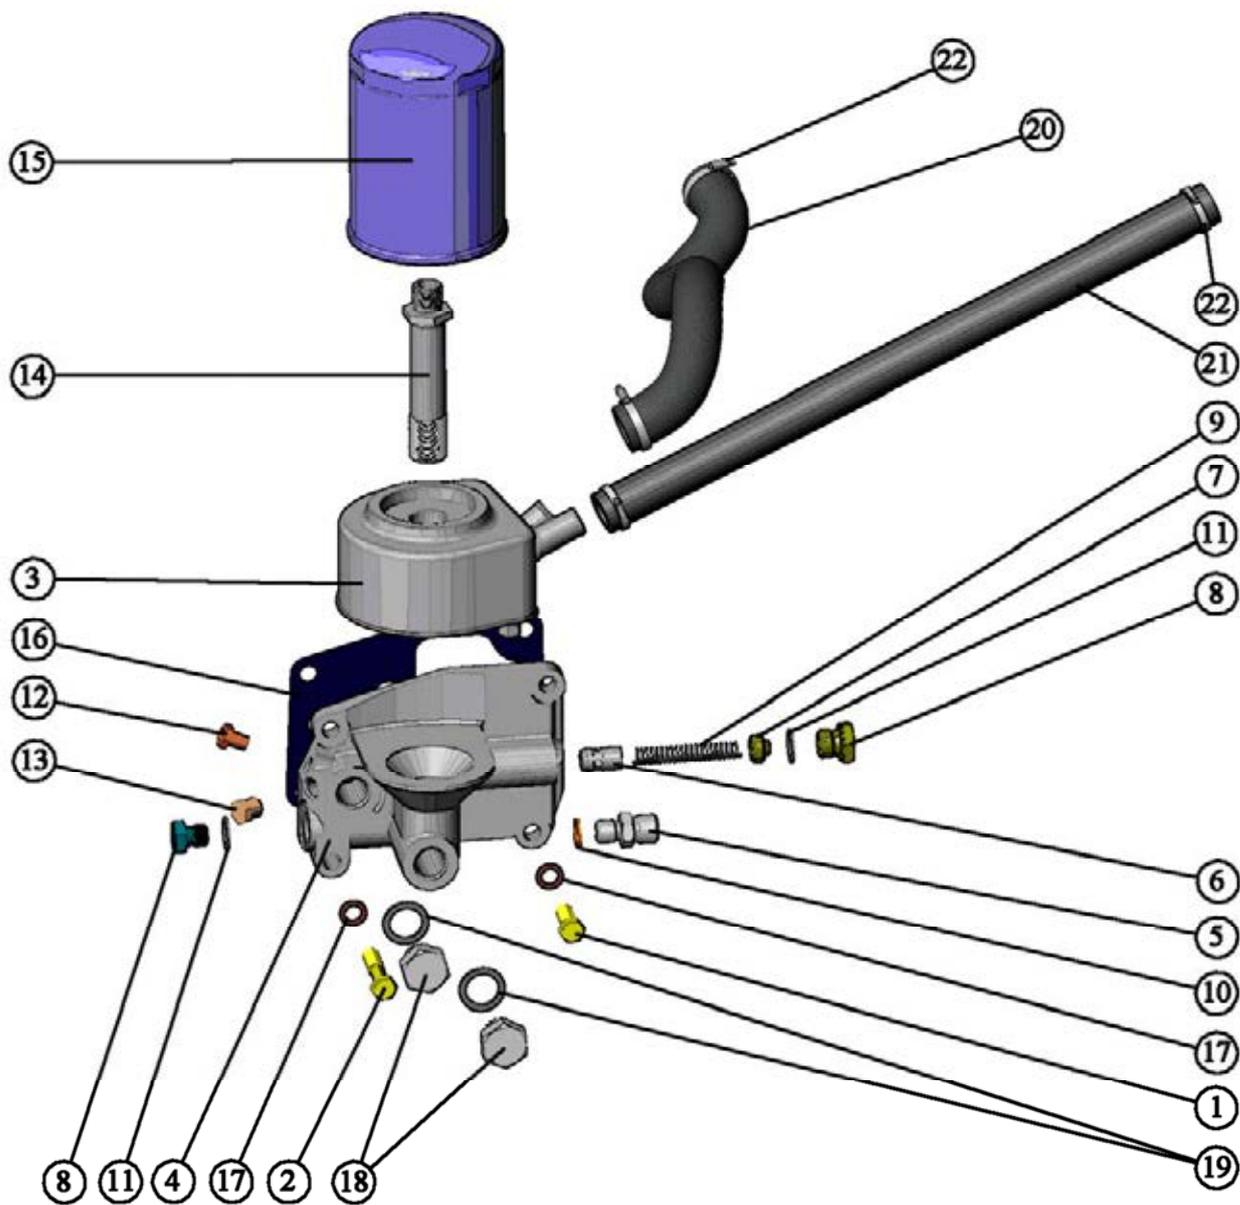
Установка фильтра с ЖМТ. Установка патрубков
